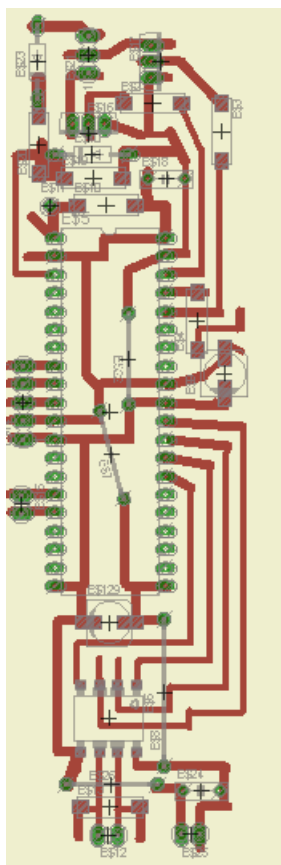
Placa PCB maestro de zona SAPOST (parte b).
